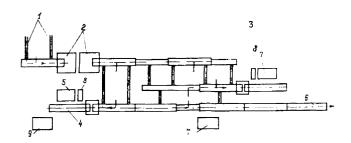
Схема трубосварочной базы БТС-143: 1-магазин труб; 2-станки для обработки кромок; 3-стенд для сборки и сварки двухтрубных секций; 4-стенд для сборки и сварки трехтрубных секций; 5-блок питания; 6-направление и стенду контроля; 7-влектростанция ими траксформаторная подстанция; 8-компрессор; 9-блок вспомогательный
